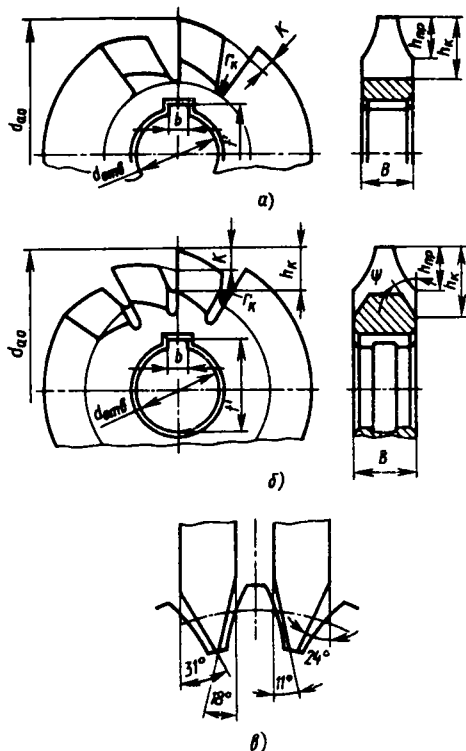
Дисковая зуборезная фреза с прямой (а) и подфрезерованной по бокам (б) канавками; фрезы для черновой обработки с прямолинейным профилем режущих кромок (в)
